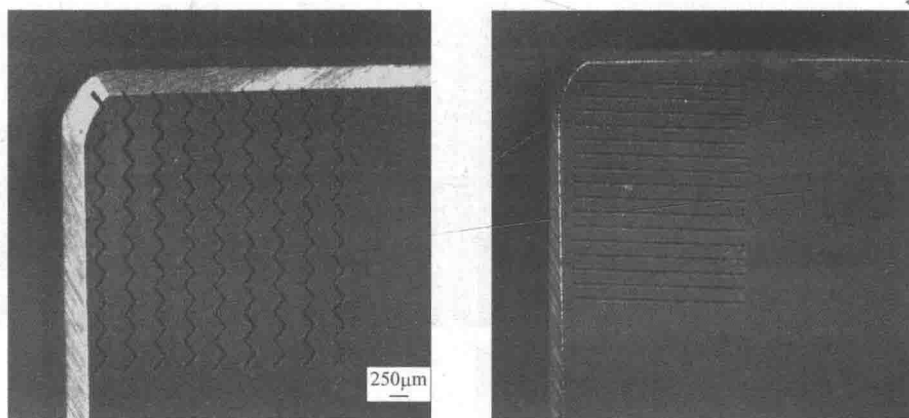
陶瓷刀具表面纳秒激光加工的微结构形貌
